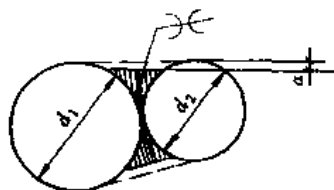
圆钢与圆钢间的连接焊缝
